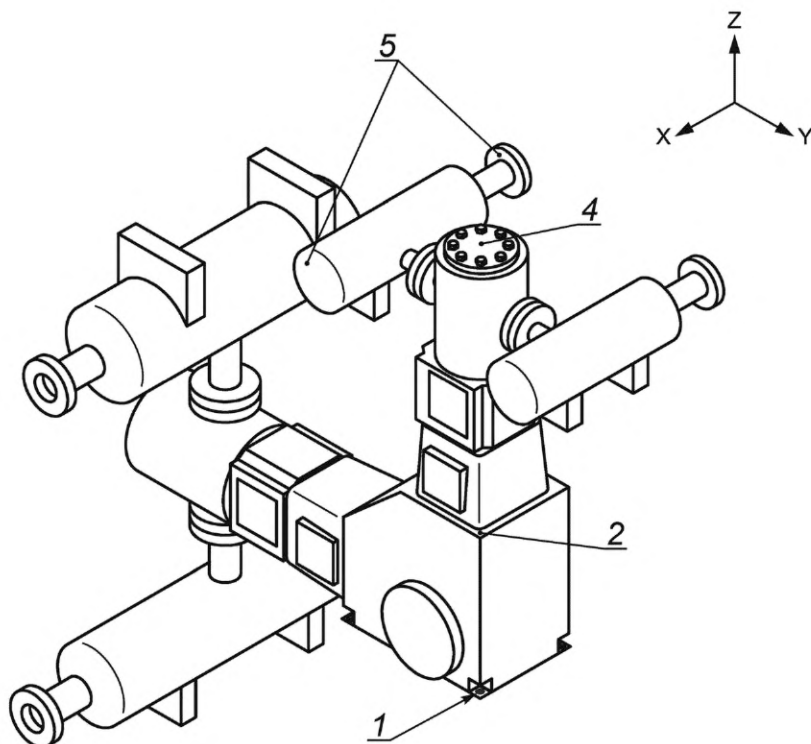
Точки измерений на компрессоре с V-образным расположением цилиндров
